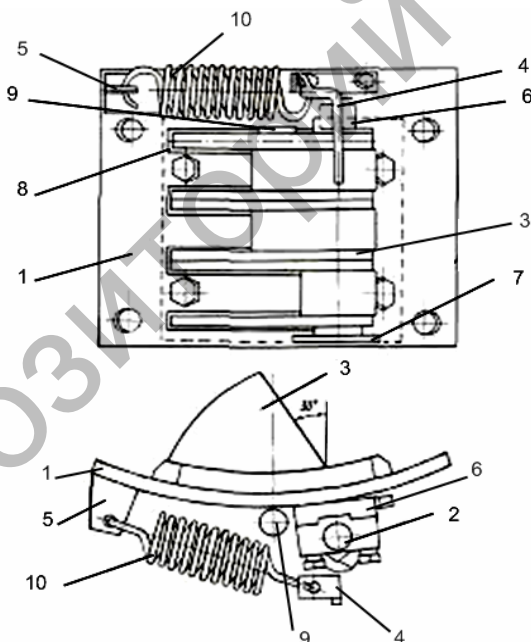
Пакет ножей-противорезов измельчителя:
